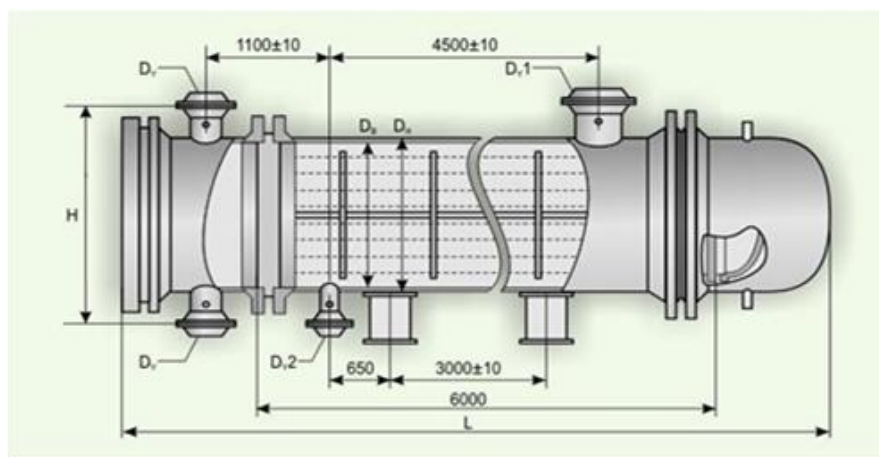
Горизонтальний дефлегматор типу КПГ з плаваючою
